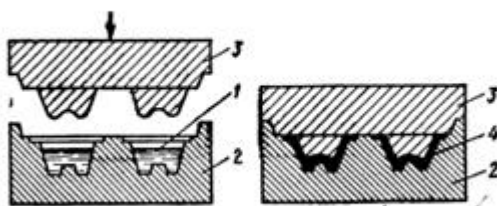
Схема жидкой штамповки. а) – заливка металла; б) - штамповка
